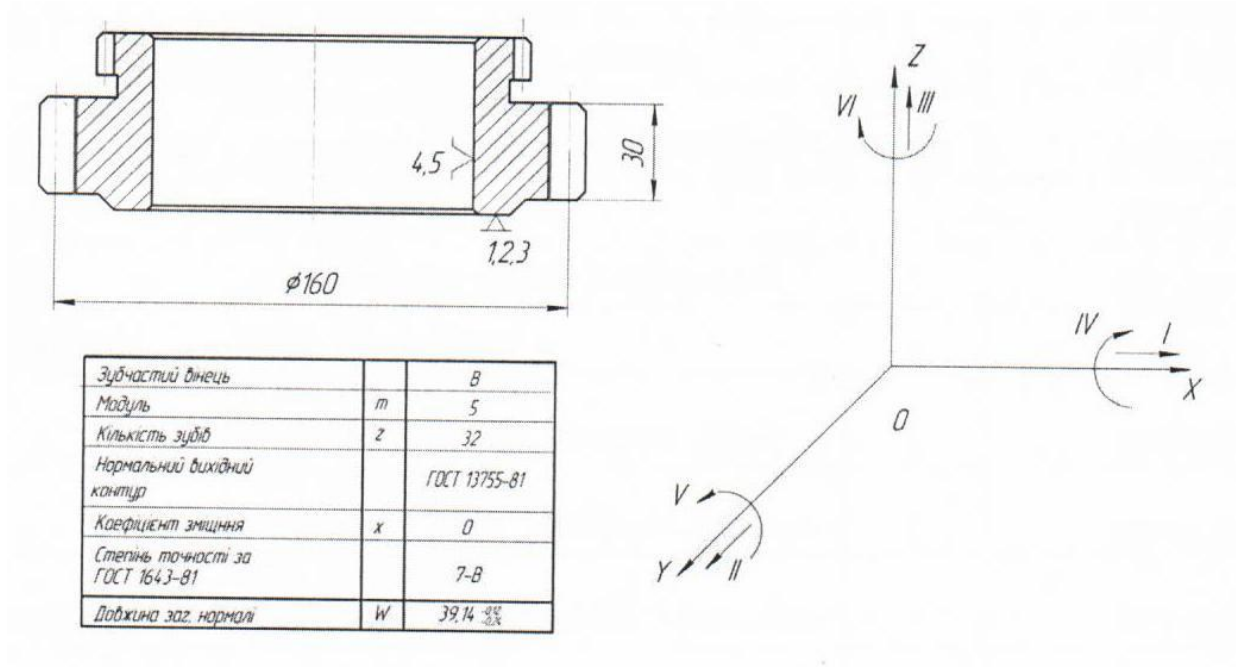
Схема базування для обробки на вертикально-фрезерному верстаті
